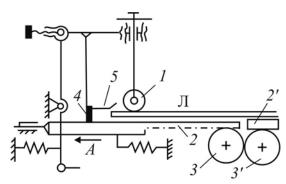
Схема механизма бокового выстойного равнения: I — обрезиненный ролик; 2 — подвижная планка; 3 — зубчатый привод планки; 4 — упор; 5 — приклон-козырек; Π — лист
